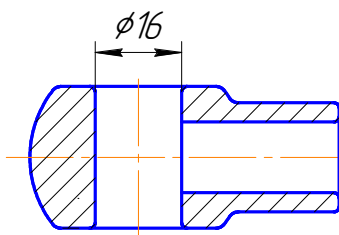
Эскиз отливки для расчета размера полости пресс-формы, образованной внутренним размером отливки
